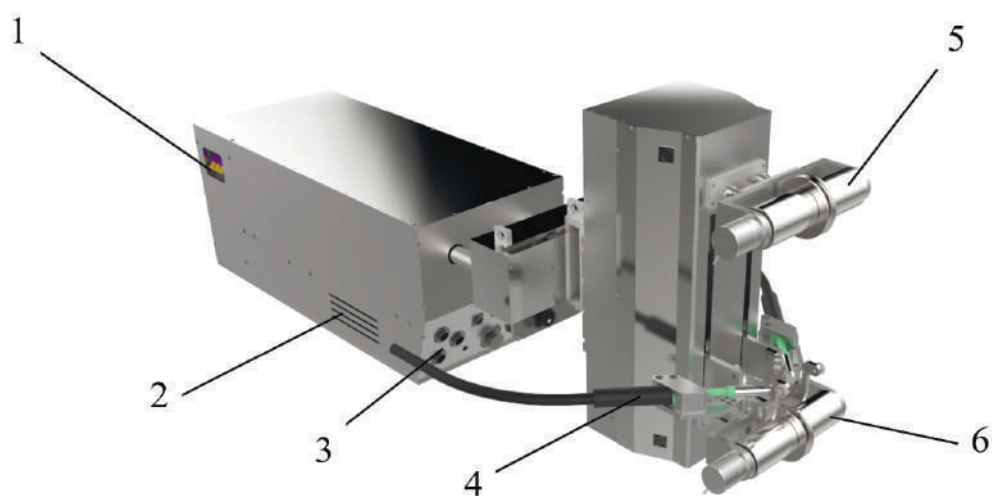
б. Схема устройства автоматического сварочного робота: 1 – выключатель питания, 2 – отверстия для охлаждения, 3 – порт для кабеля управления, 4 – сварочная горелка, 5 – верхний ролик поперечной арматуры, 6 – нижний ролик поперечной арматуры
